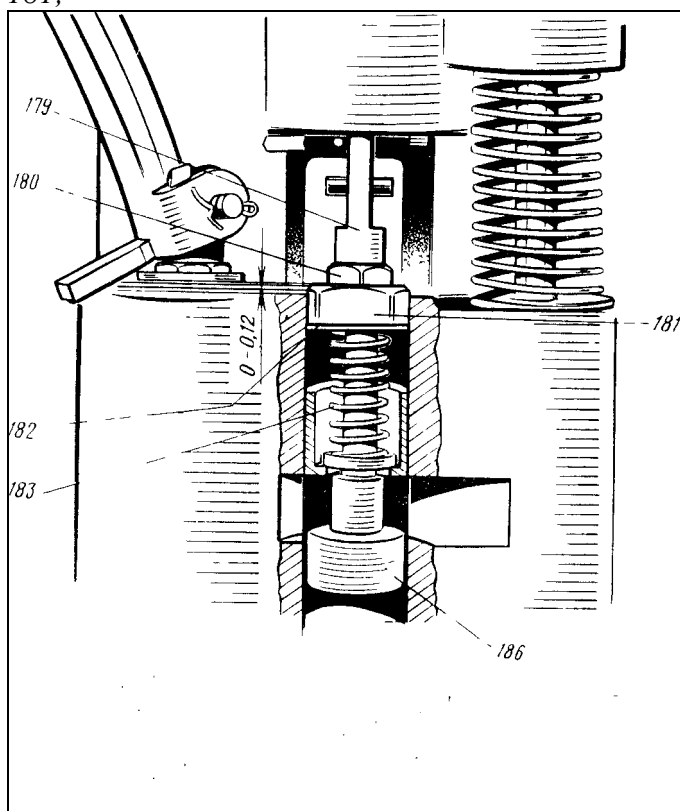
179—наконечник штока принимающего поршня изодрома; 180—контргайка штока; 181—верхняя упорная тарелка пружины изодрома; 182—шайба для регулирования натяжения пружины изодрома; 183—пружина изодрома; 186—принимающий поршень изодрома
